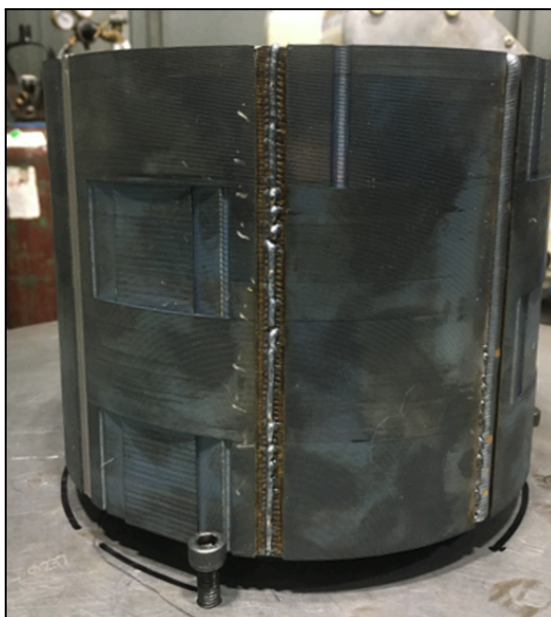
Estatores bobinados soldados com MIG e lixados com disco flap.
